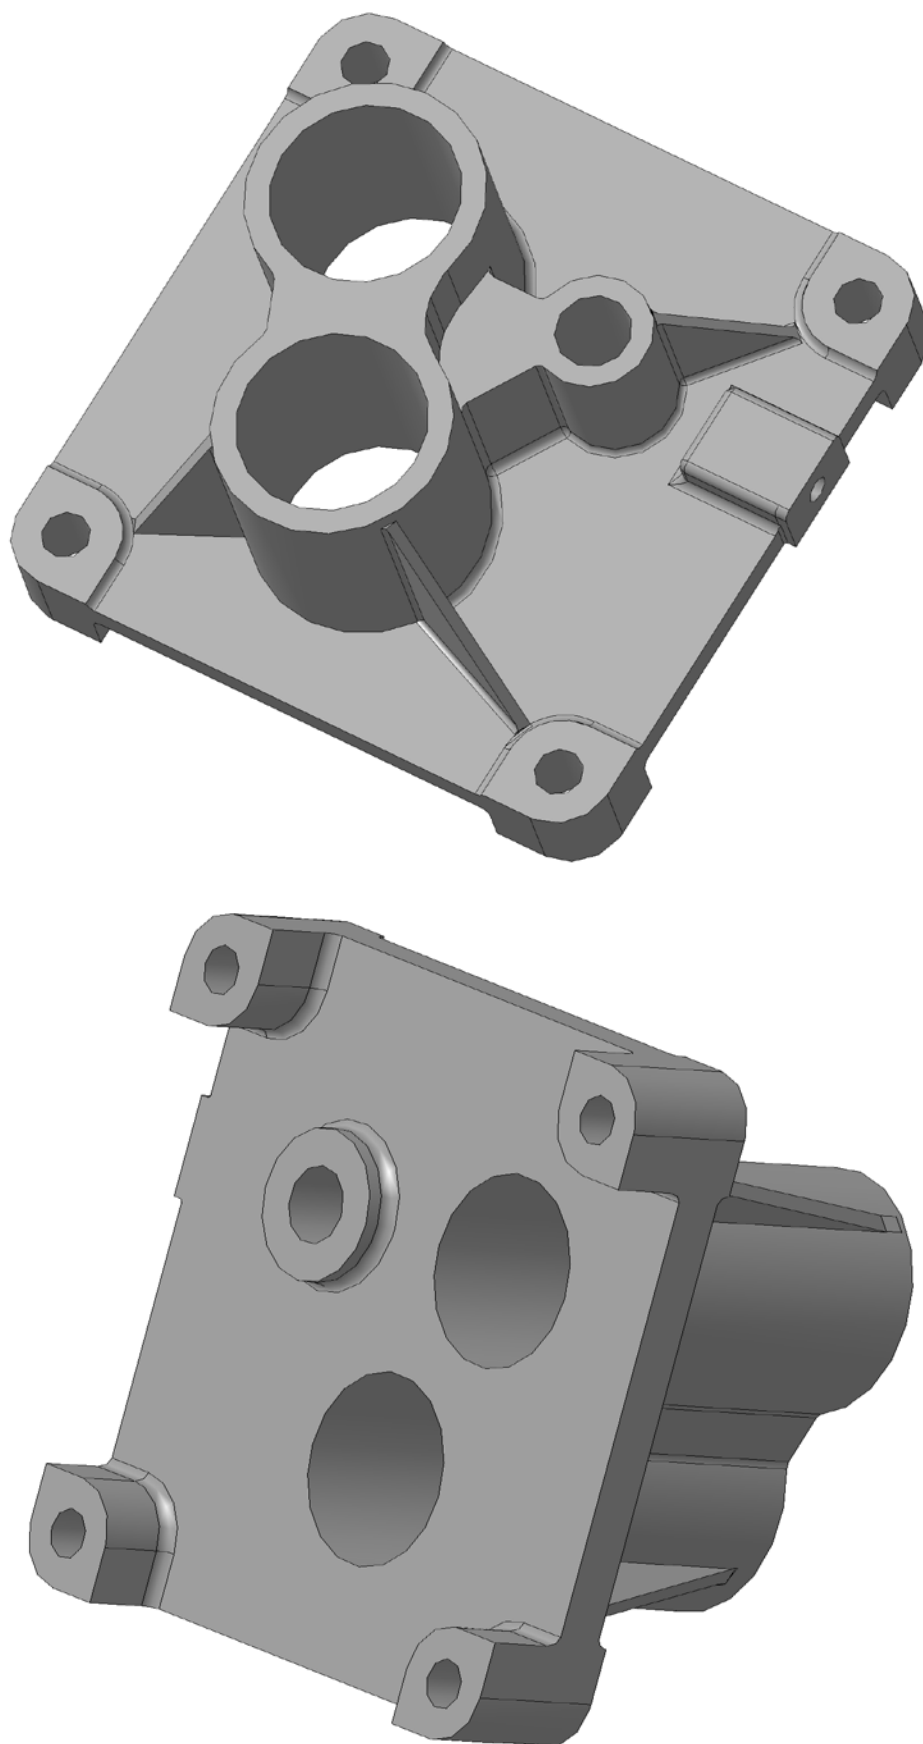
3D модель детали «Корпус подшипника тягового механизма»
